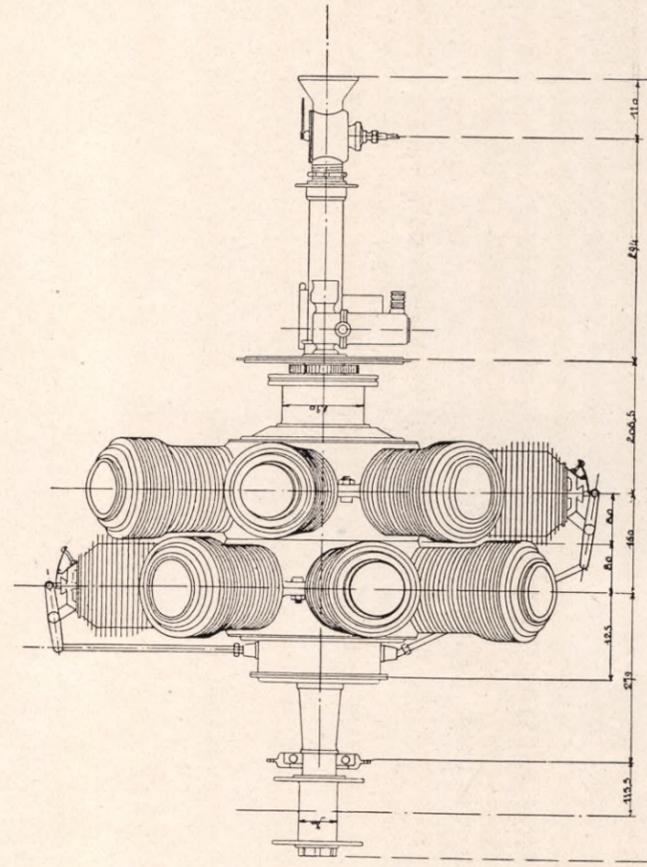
120 P 14-Zylindermotor, Raumzeichnung, Seitenansicht.
